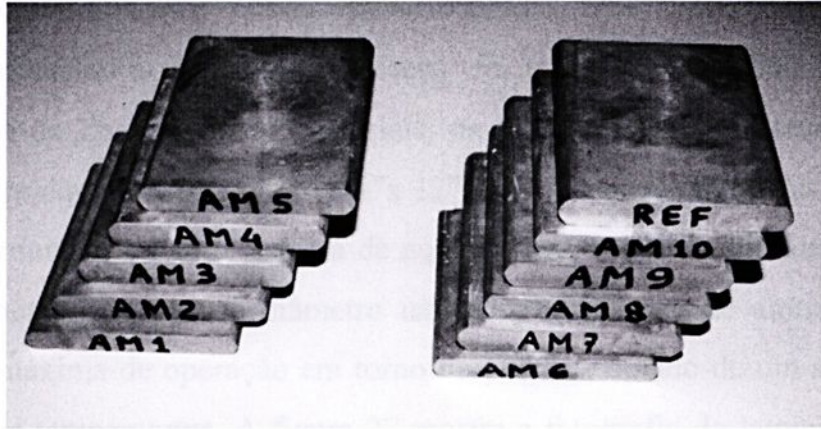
Geometria das placas usinadas, prontas para a laminação a quente.
